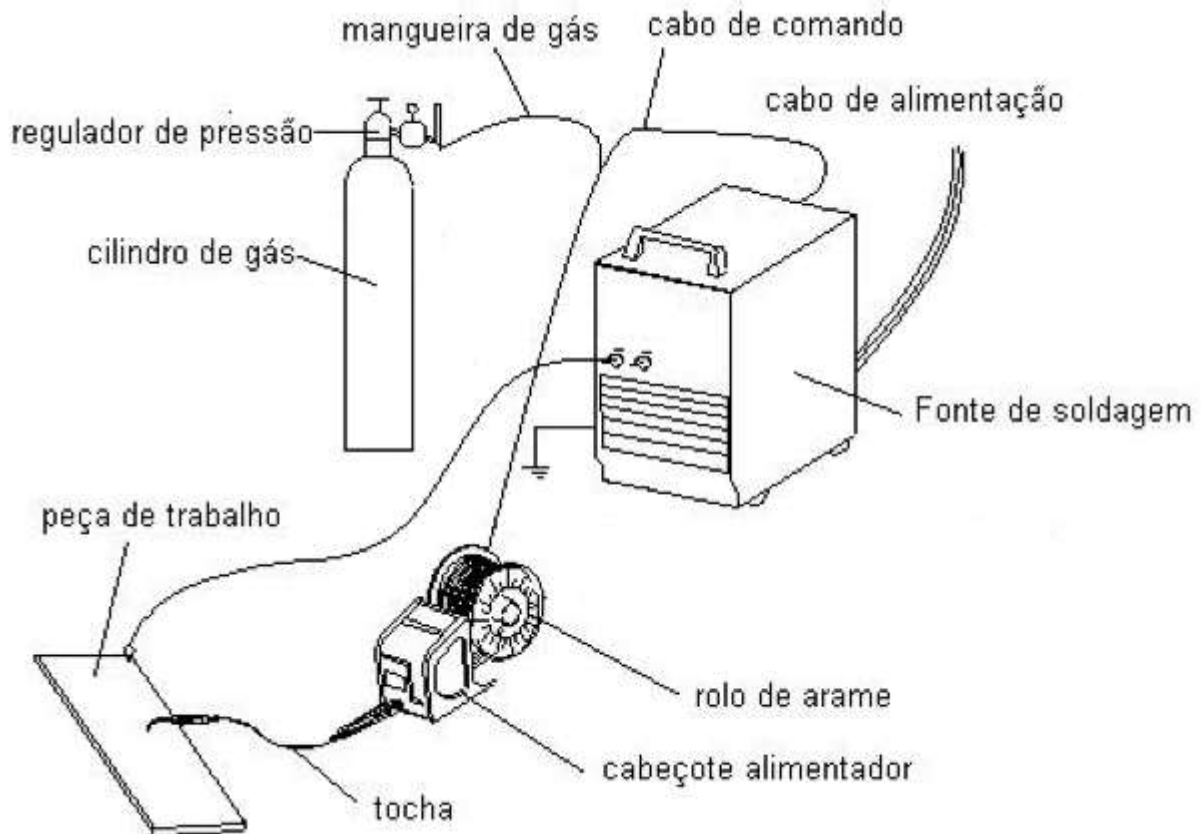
Diagrama conexão soldagem MIG/MAG.
